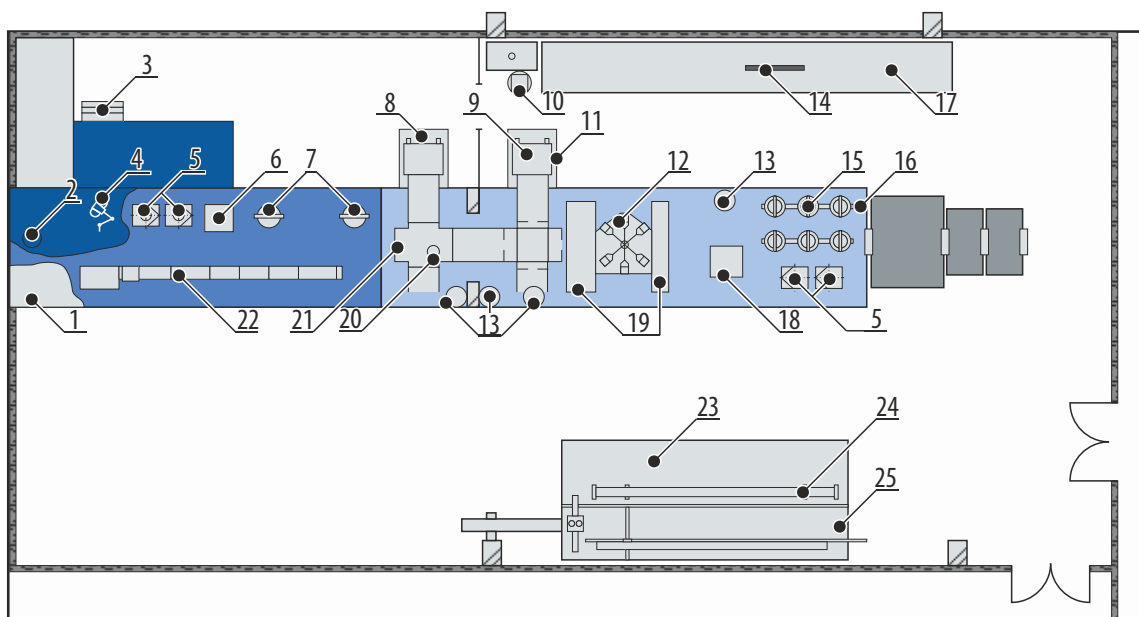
Схема расположения оборудования на участке изготовления ТВЭЛов: 1 — участок виброуплотнения ТВЭЛов; 2 — устройство транспортное вертикальное; 3 — подставка для ТВЭЛов; 4 — смеситель; 5 — фильтр вытяжной вентиляции (4 шт.); 6 — устройство отбора пробы гранулята; 7 — участок установки прокалки гранулята; 8 — форкамера левая (выгрузочная); 9 — тележка форкамеры; 10 — установка дезактивации ТВЭЛов; 11 — форкамера правая (загрузочная); 12 — установка фасовочно-дозировочная; 13 — разметка на столешнице для топливных контейнеров (4 шт.); 14 — контейнер для ТВЭЛов реактора БОР-60; 15 — платформа для топливных контейнеров; 16 — перчаточный бокс; 17 — стол рабочий; 18 — весы; 19 — поддон для рабочих контейнеров; 20 — тарелка для топлива; 21 — большая тележка бокса; 22 — передвижное горизонтальное устройство; 23 — настил установки «Аккорд-4»; 24 — контейнер для ТВЭЛов реакторов БН-600 и БН-800; 25 — стол установки «Аккорд-4»³;
